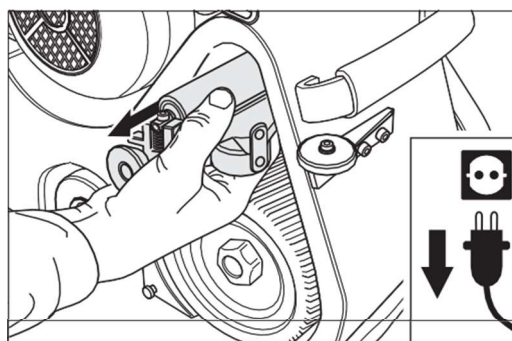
Das Aggregat vorsichtig aus dem Maschinengehäuse
